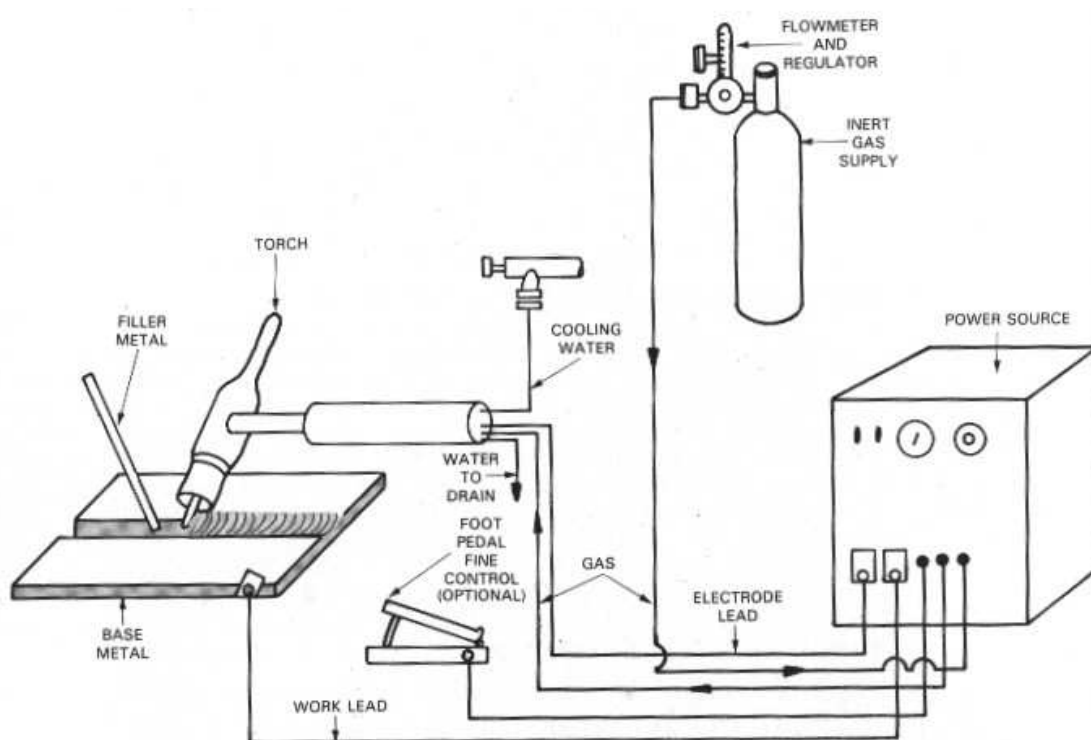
Processo de soldadura TIG [1].
